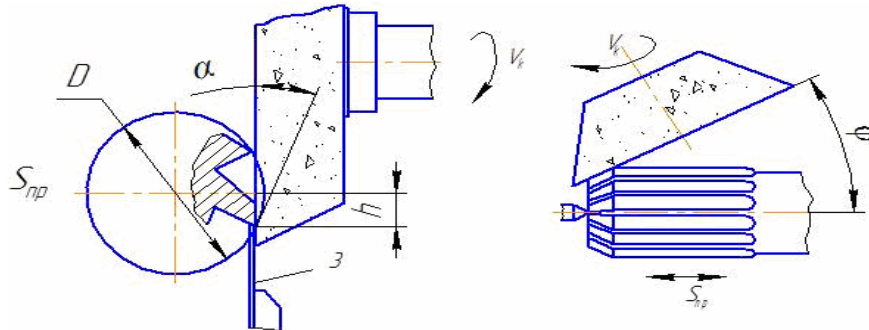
Схема заточування розвертки по задній поверхні на різальній частині
